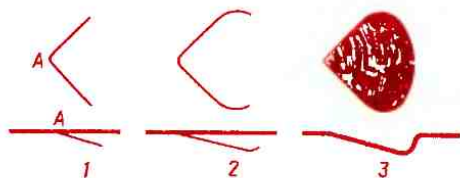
Схема образования поверхностного выкрашивания (питтинга) на рабочей дорожке подшипника качения:
